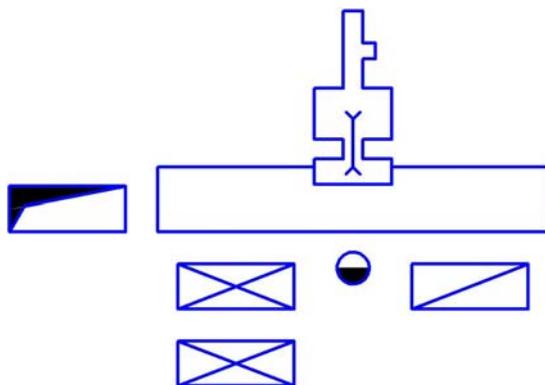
Организация рабочего места станка суппортного ЦПА40 с прямолинейным возвратно-поступательным движением пильного суппорта для чистового поперечного раскроя деталей
